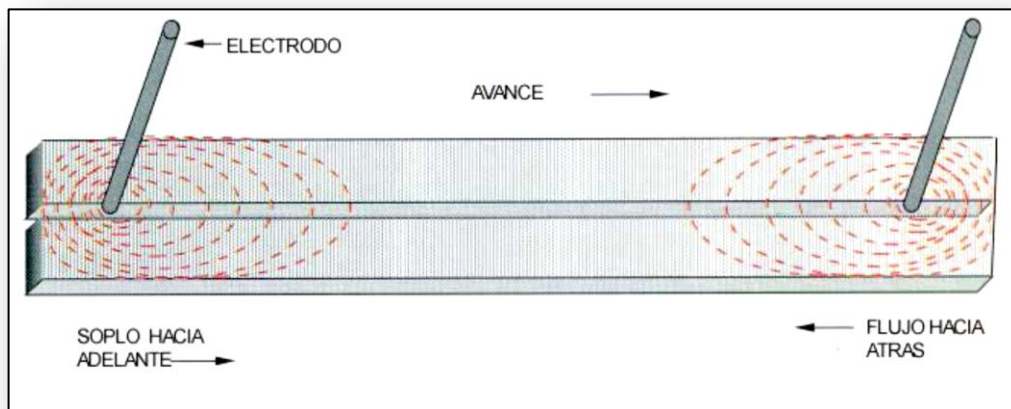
Campos Magnéticos Distorsionados en los Extremos de la Soldadura.¹²
